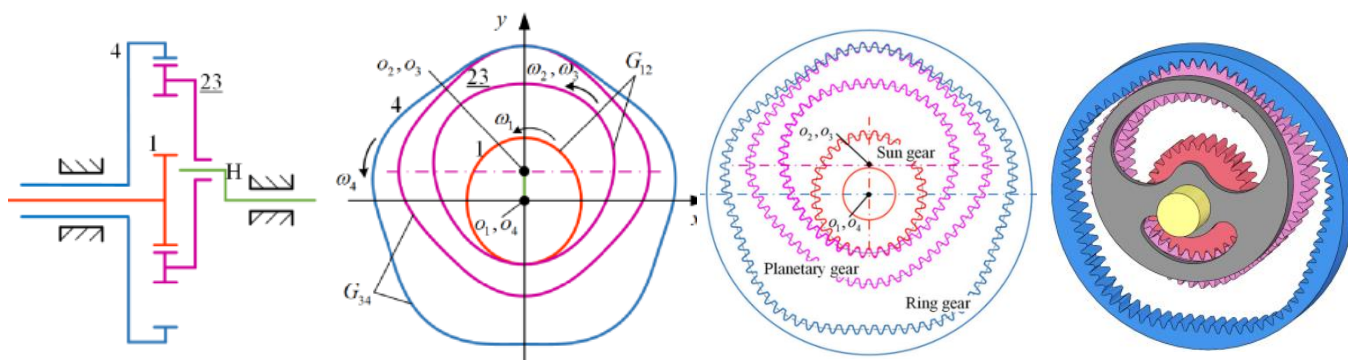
Основная конструкция планетарной передачи с некруглыми колесами, соосным расположением и двойным внутренним зацеплением: 1-солнечная шестерня; 2, 3 - планетарные шестерни; 4- кольцевая шестерня; Н – водило.
